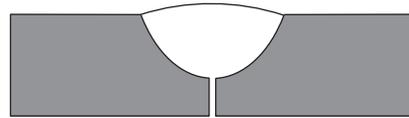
Exemple de soudure incorrecte n° 7
